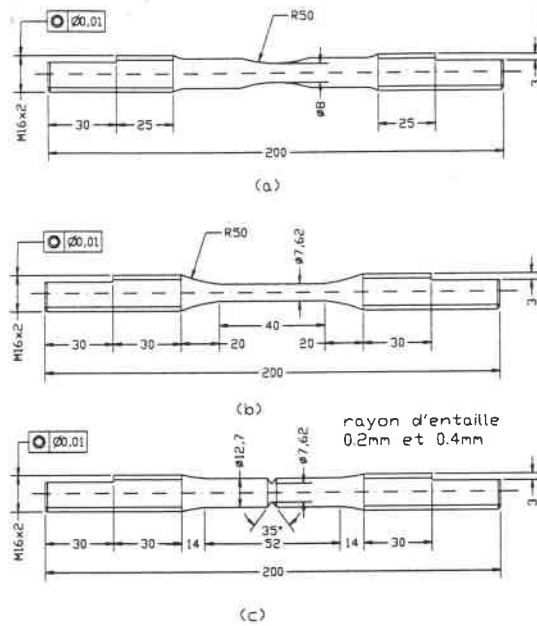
Dessin des éprouvettes entaillées et lisses : a) éprouvette lisse chargée en torsion
